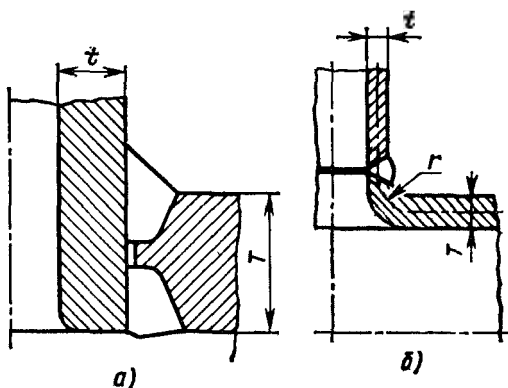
Конструкции соединения корпуса и штуцера: а — прямое примыкание (варка); б — примыкание через отбортовку корпуса
